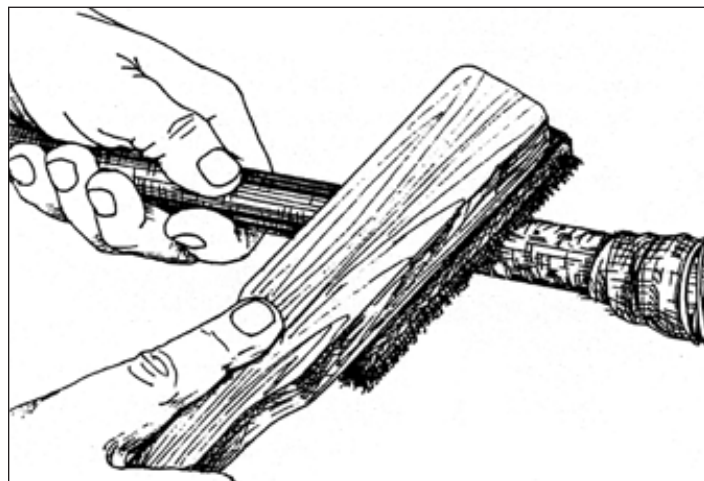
Зачистка алюминиевой оболочки металлической щеткой
